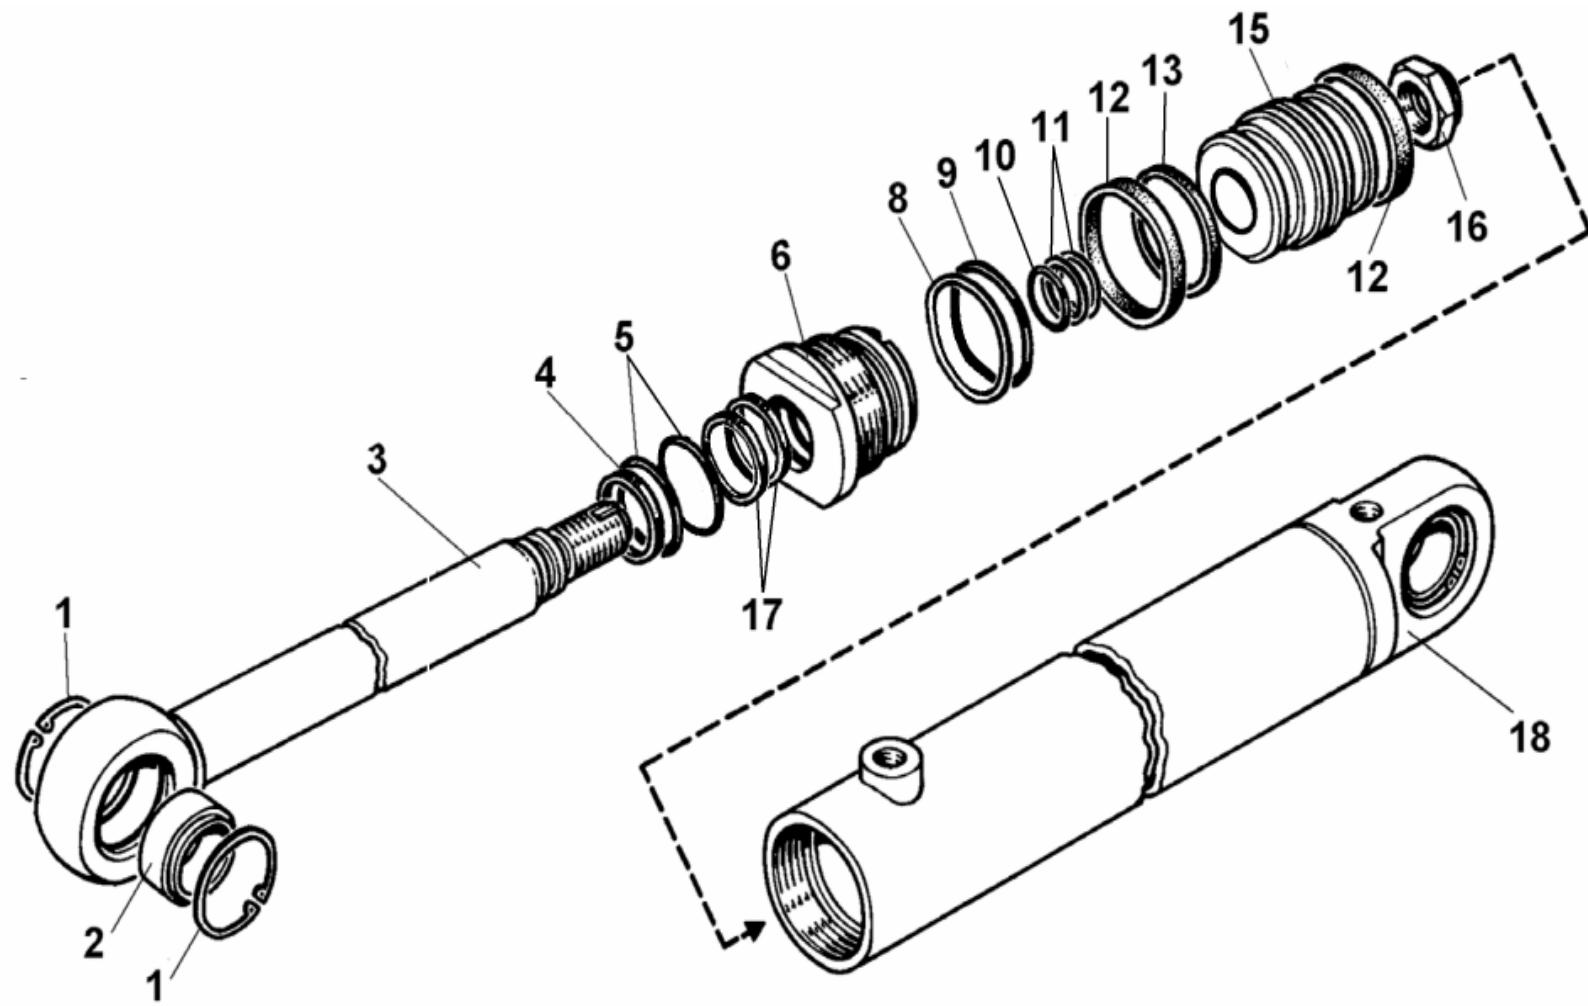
208A.45.05.500-03	Гидроцилиндр поворота ковша
